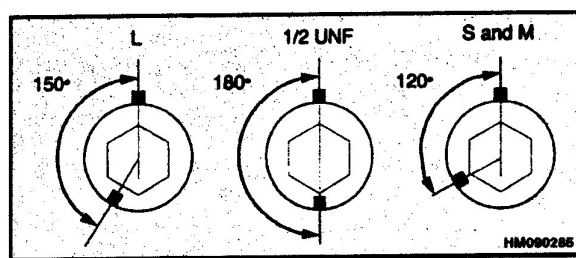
Подтяжка болтов крышки цилиндра, двигатель типа AR
